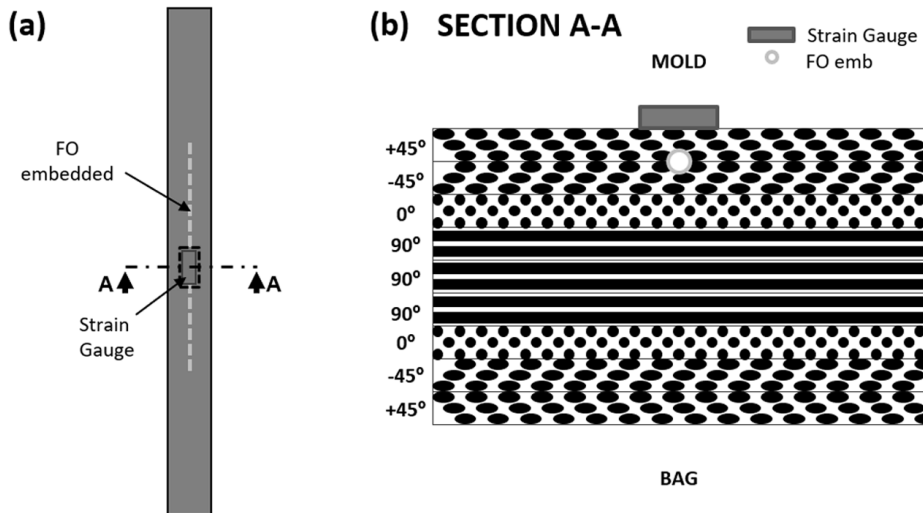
Probeta ensayo tracción instrumentada con fibra óptica embebida y galga: (a) esquema de fabricación en planta y (b) corte trasversal A-A.
